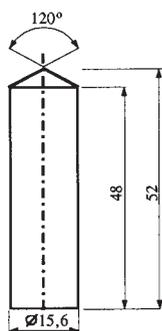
Цилиндрический бронзовый поршень; размеры в мм
